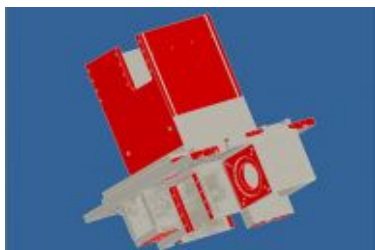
Obráběcí stroj MC6 – 250 [14]
